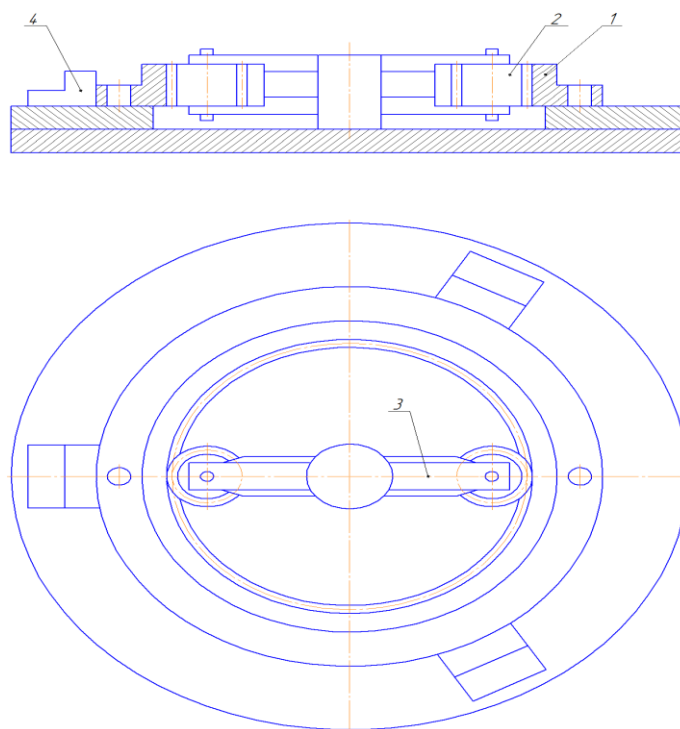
Приспособление для обработки ППД зубчатого венца
